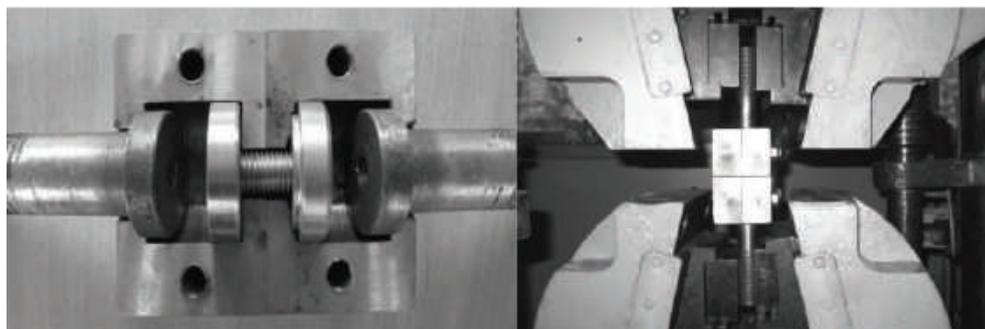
Оснастка для механических испытаний на разрыв крепежных элементов
